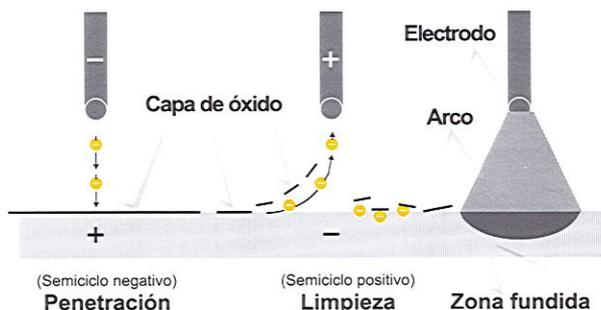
Polarización con corriente alterna en proceso de soldadura TIG (GTAW).
